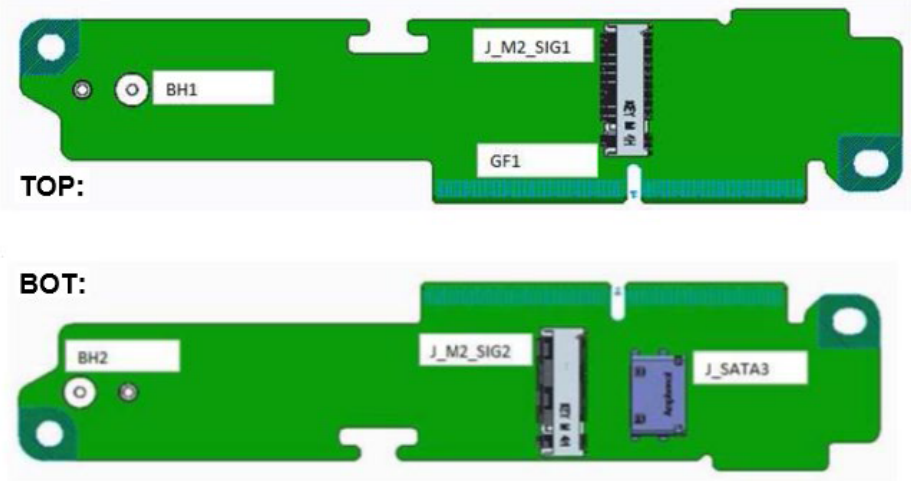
M.2 X 16 SATA 提升板 PCB 尺寸
